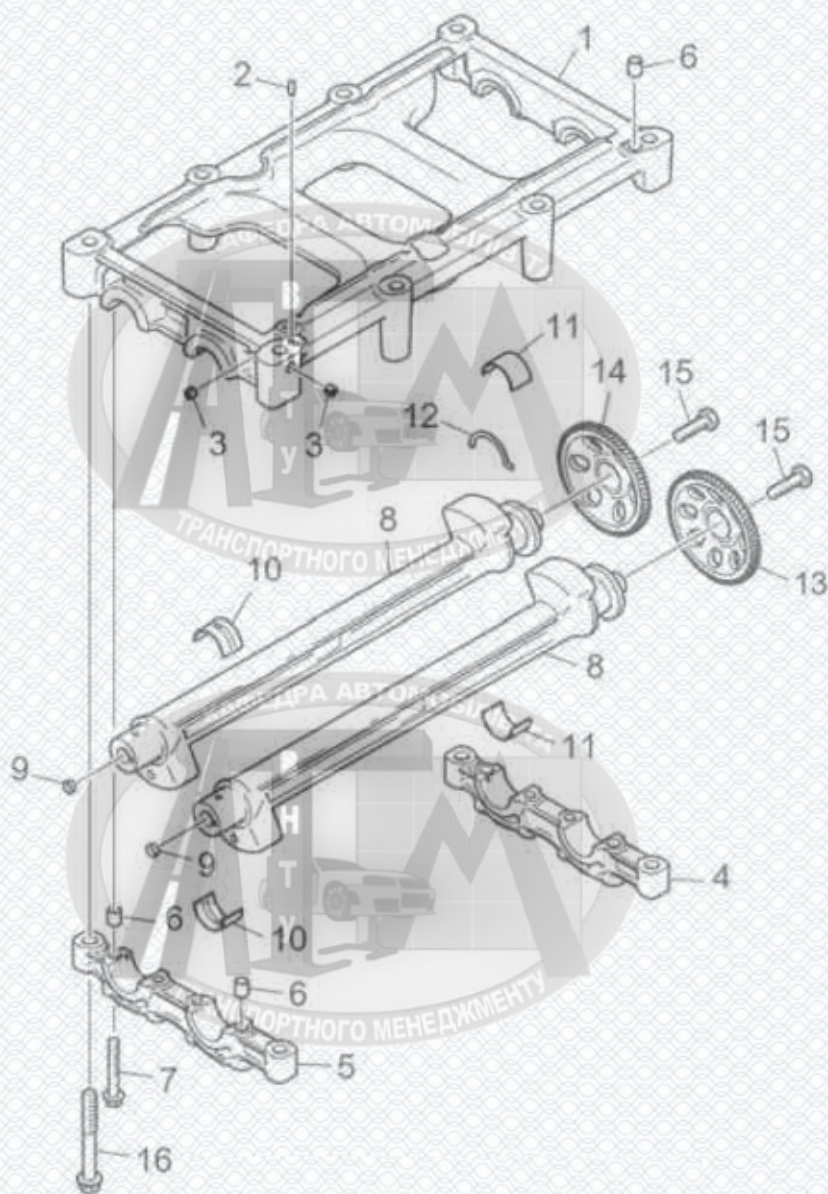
Конструктивні особливості блоку врівноважувальних валів: 1 – рама блоку системи врівноваження; 2 – штифт; 3 – різьбова пробка; 4, 5 – кришка нижньої головки шатуна; 6 – напрямна втулка; 7 – болт; 8 – балансірний вал; 9 – заглушка; 10, 11 – радіальний підшипник; 12 – упорний підшипник; 13, 14 – шестерня валу системи врівноважування; 15, 16 – болти.
